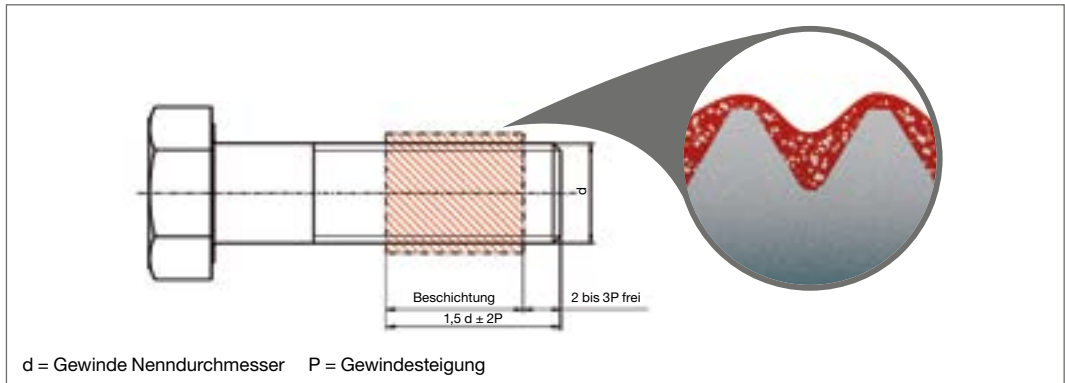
Position der Beschichtung am Beispiel einer Sechskantschraube
